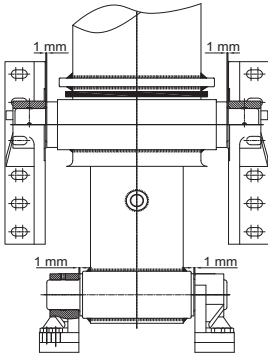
C Tipi Üçgen Braket Bağlantısı - Boşluk Gösterimi
